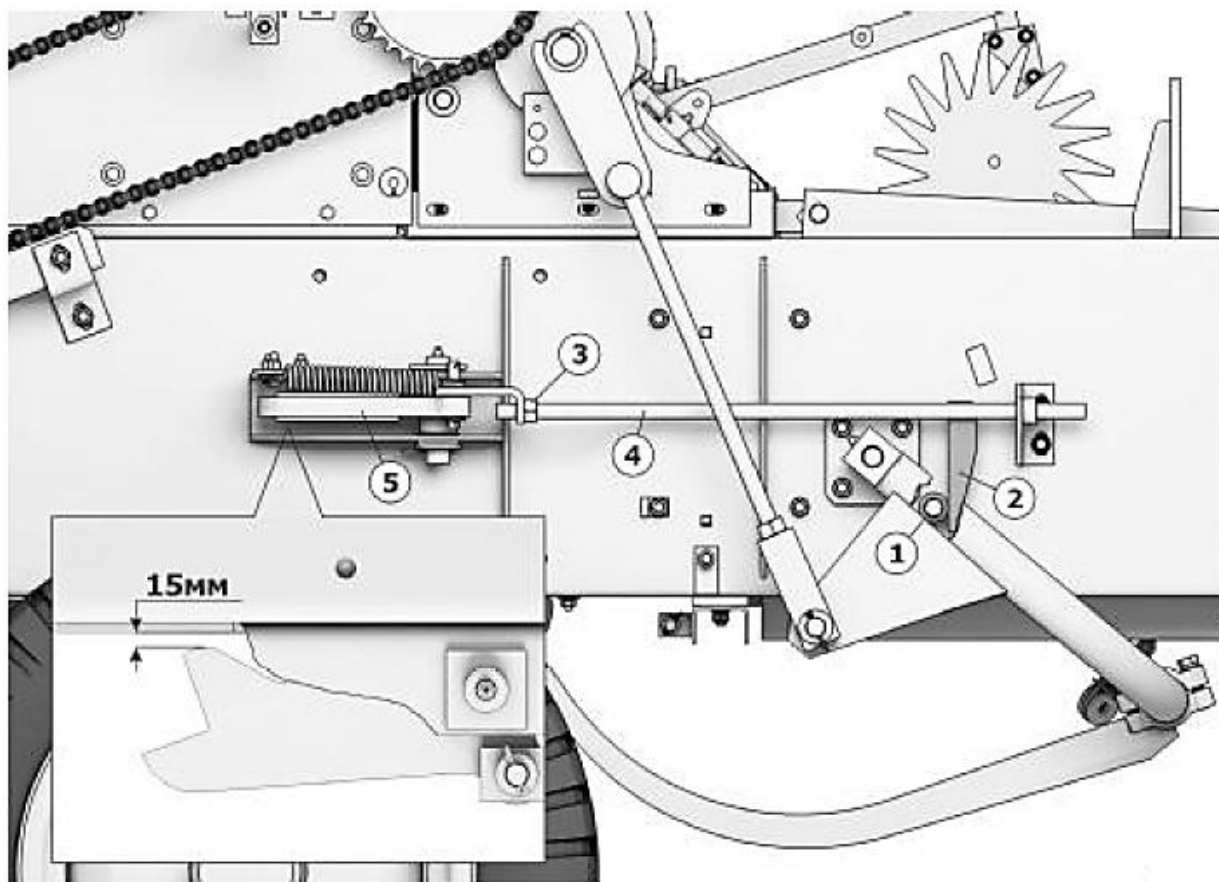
Установка предохранителя: 1 – ролик; 2 – уголок; 3 – гайка; 4 – тяга регулируемая; 5 – предохранитель
